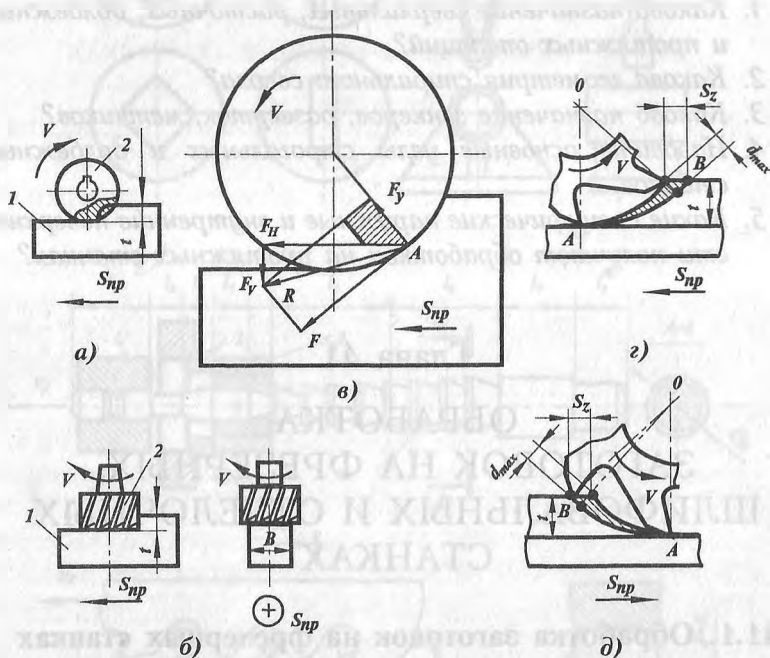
Схемы фрезерования: *a, д* — попутное; *б* — торцевое; *в, з* — встречное
